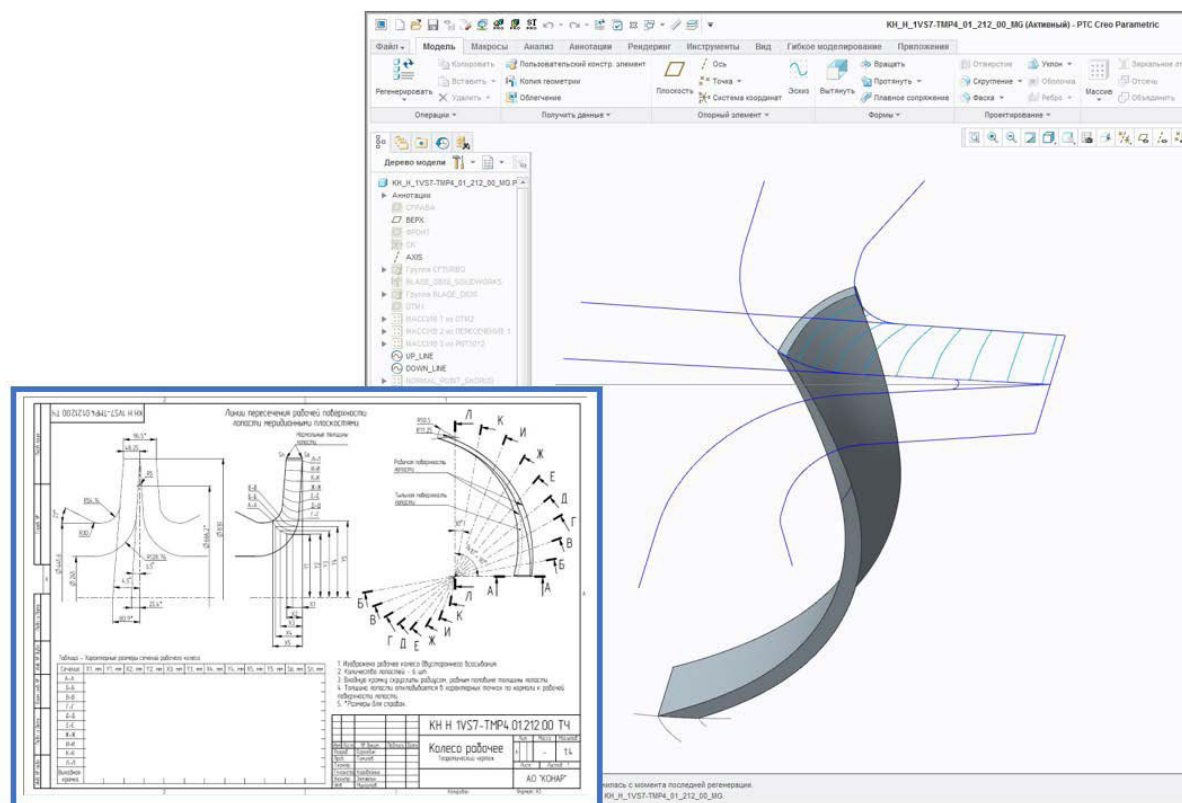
3D-модель теоретической геометрии и теоретический чертеж
